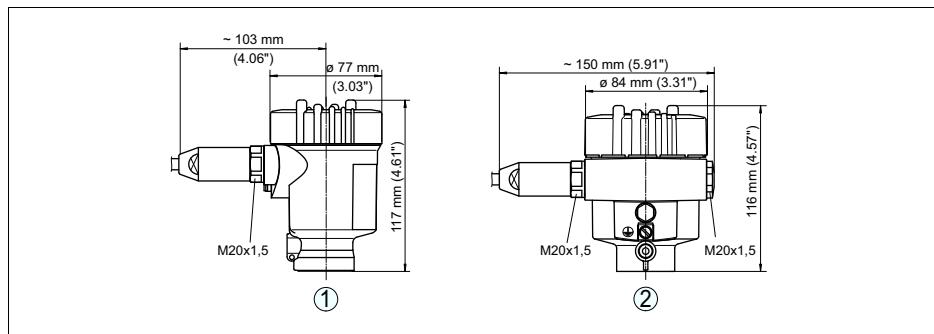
Исполнения корпуса со степенью защиты IP 66/IP 68 (1 bar)
